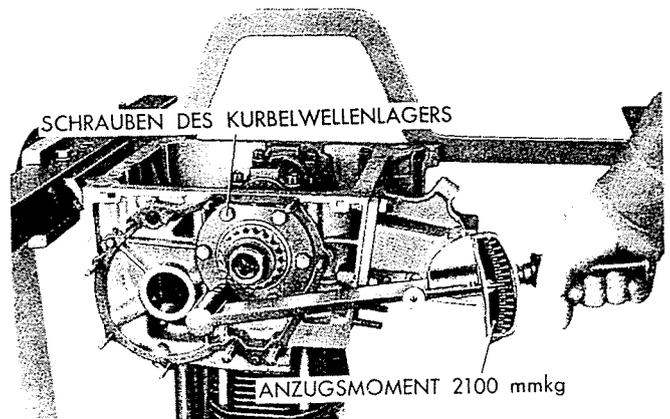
Dynamometerschlüssel zum Anziehen der Schrauben des Kurbelwellenlagers (Steuergehäusesseite).
